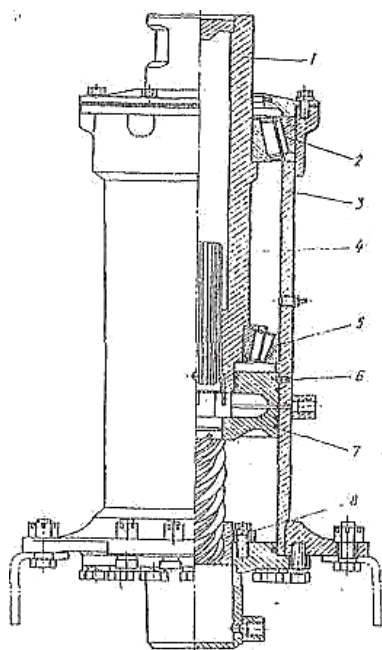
Механизм поворота крана: 1 – стойка; 2, 5 – конические подшипники; 3 – корпус; 4 – винт; 6 – корпус крышки; 7 – поршень; 8 – гайка
